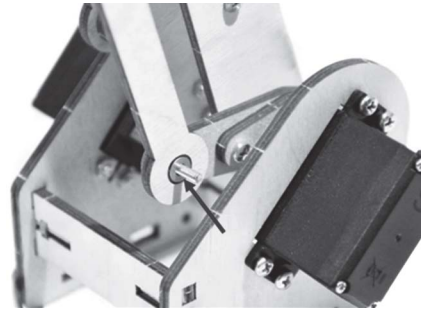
Промежуточный итог сборки крепежа стяжки 3.
